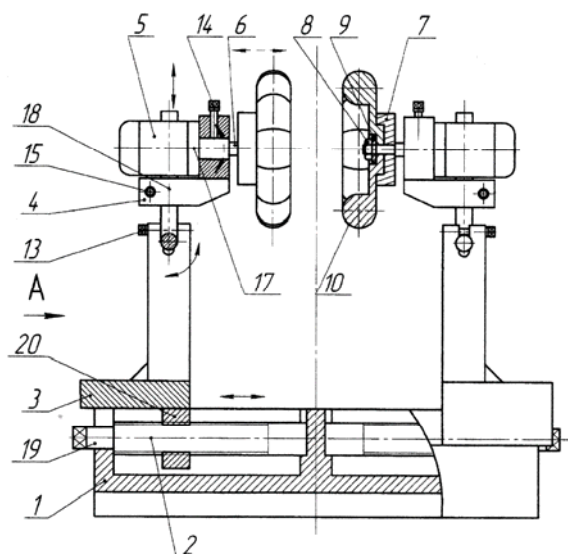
Устройство для магнитно-абразивной обработки патент RU №2220836
